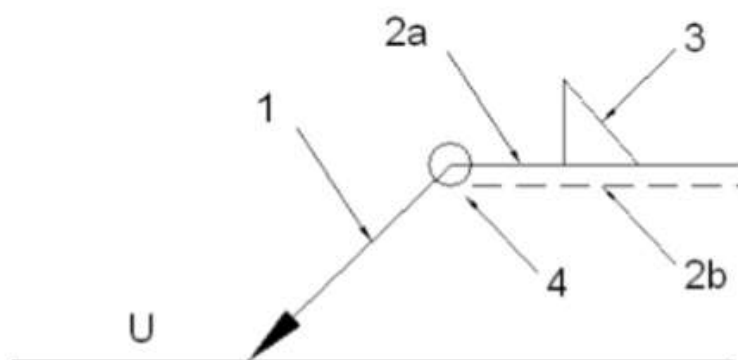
Nomenclatura soldadura. Referencias: 1: línea de la flecha 2a: línea de referencia (línea continua) 2b: línea de identificación (línea a trazos) 3: símbolo de soldadura 4: indicaciones complementarias U: Unión.
